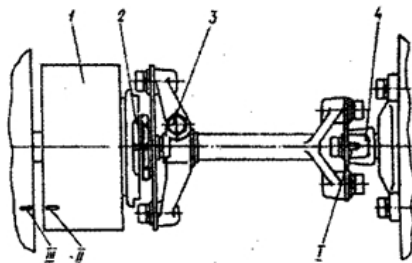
Установка топливной аппаратуры по меткам: 1 - метка на заднем фланце полумуфты; П - метка на муфте опережения впрыскивания; Ш - метка на корпусе топливного насоса; 1 - муфта опережения впрыскивания; 2 - ведомая полумуфта; 3 - соединительный вал; 4 - фланец задней ведущей полумуфты
